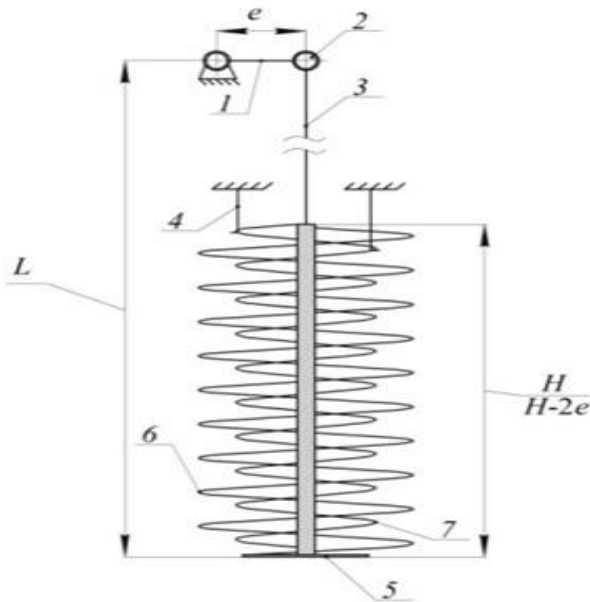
Кинематическая схема пружинного виброуплотнителя на основе пружины сжатия
